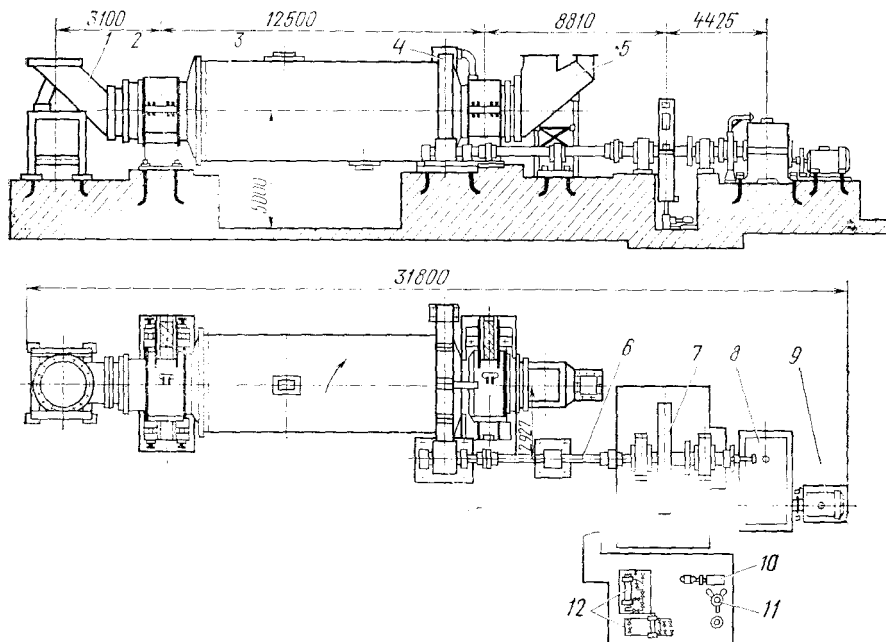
Общий вид трубной мельницы размером 4,2x10 м:
